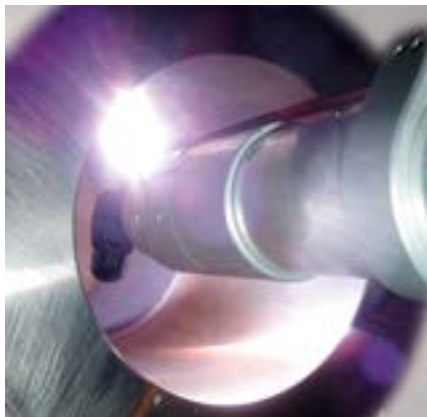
Наплавка внутренней поверхности трубы. Ширина наплавки менее 2 м, насадка оборудована одним подводом присадочной проволоки
